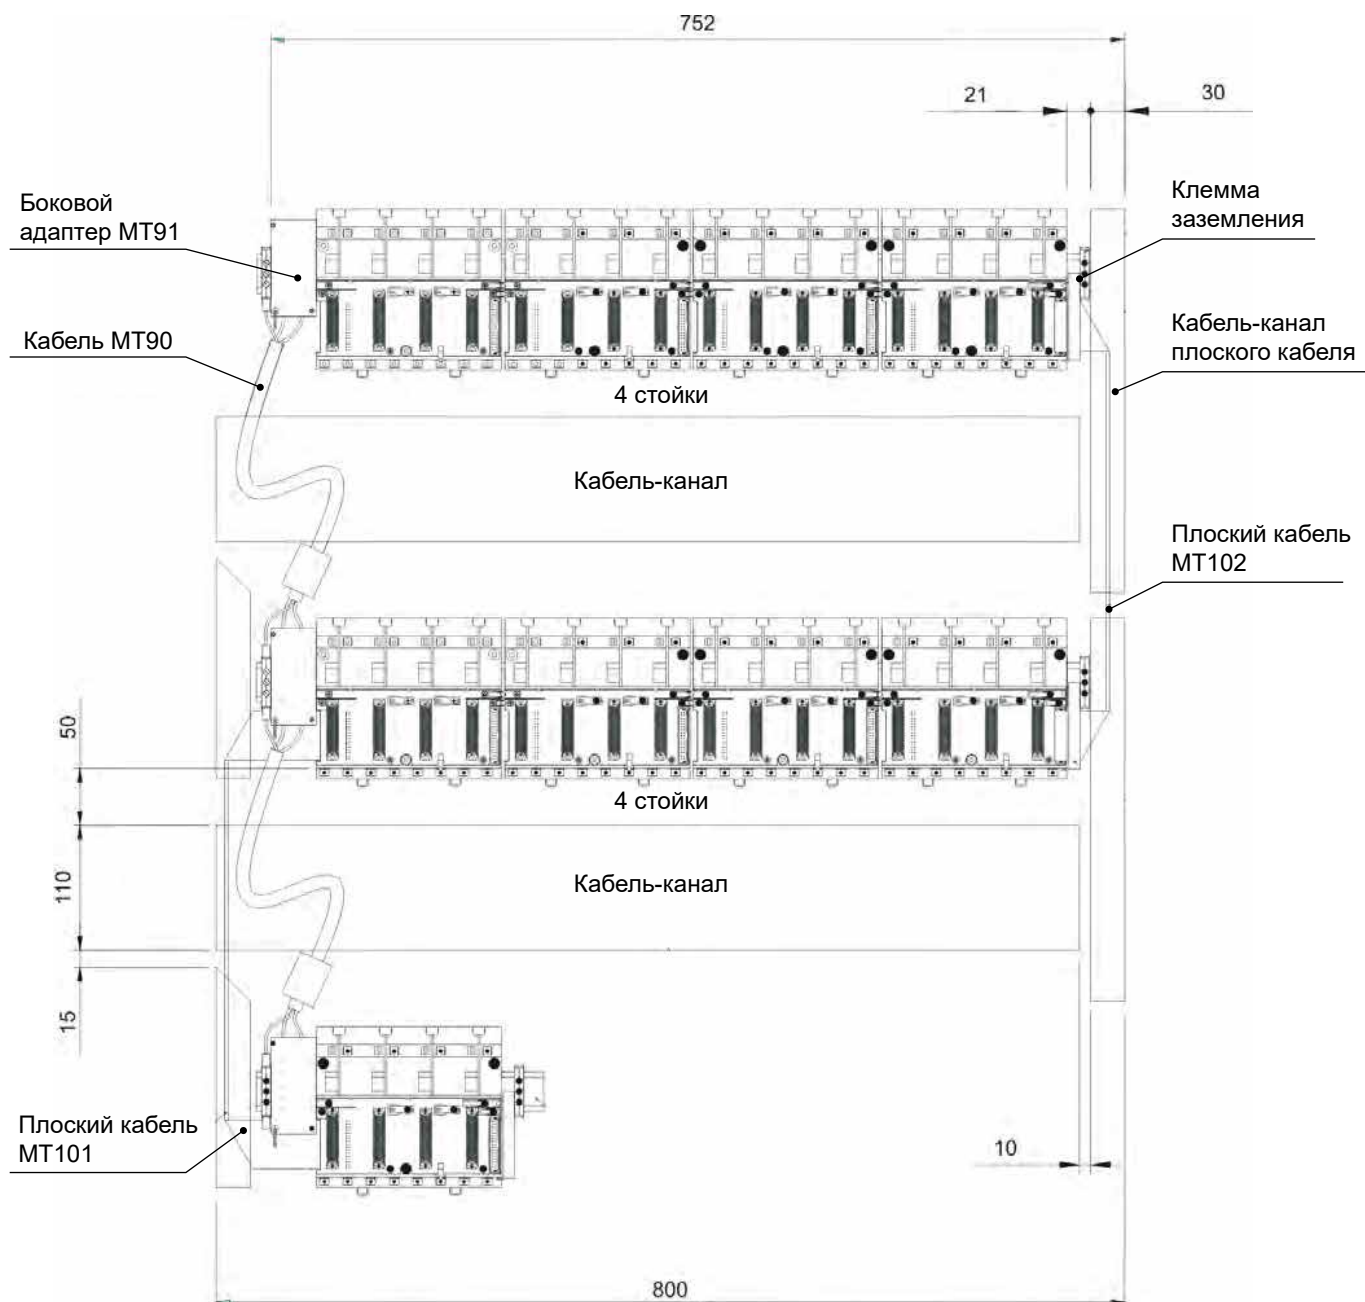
Габаритные чертежи стойки МТ93 и модулей
